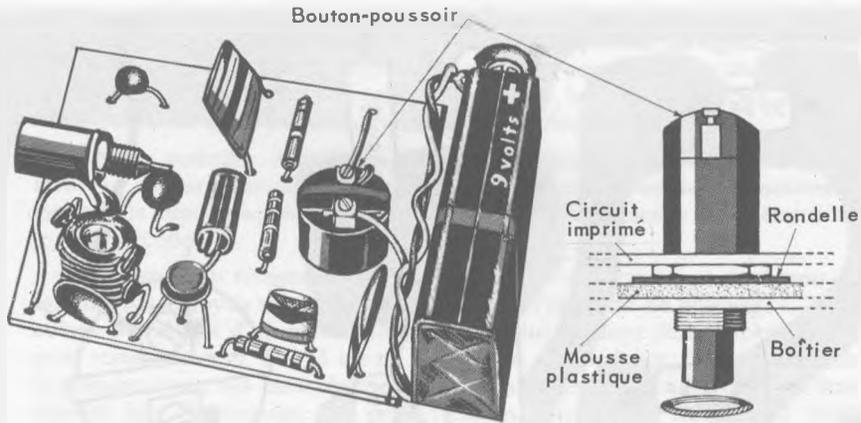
La plaquette est fixée au fond du coffret au moyen du bouton-poussoir.
